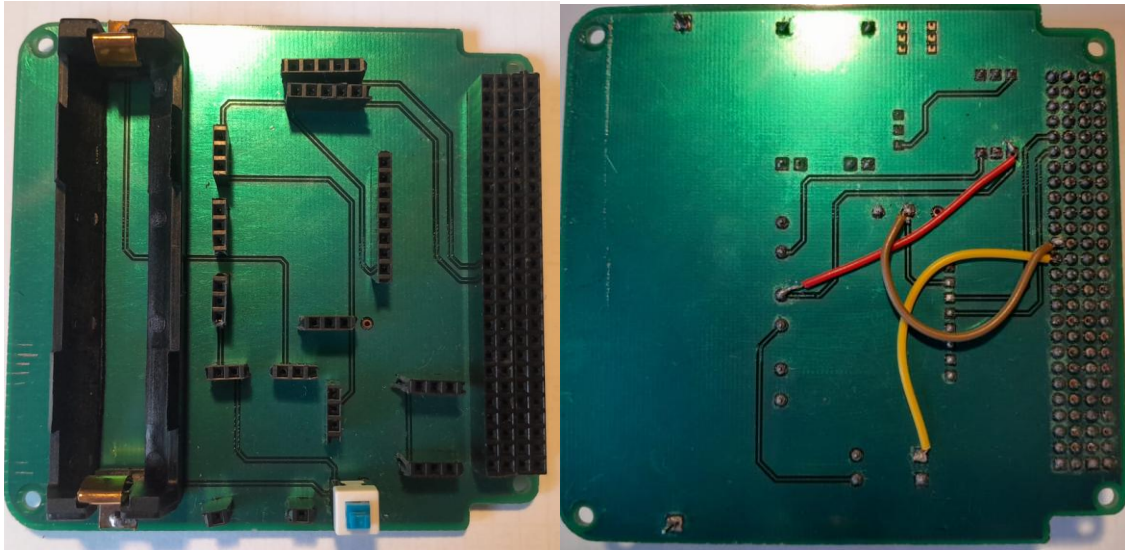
PCB del EPS con elementos de superficie soldados. Izquierda: vista superior. Derecha, vista inferior.
